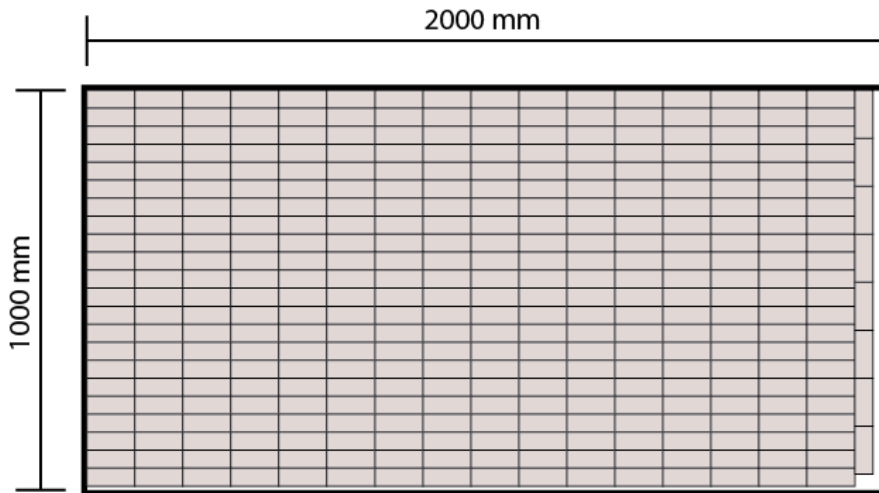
Cortes de las piezas “jaladeras” en una plancha de grilon
